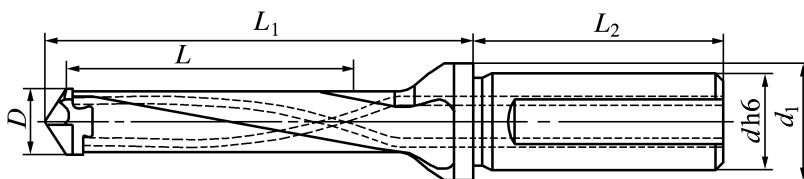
Сверла со сменными головками "CHAMDRILL" и внутренней подачей COTC
